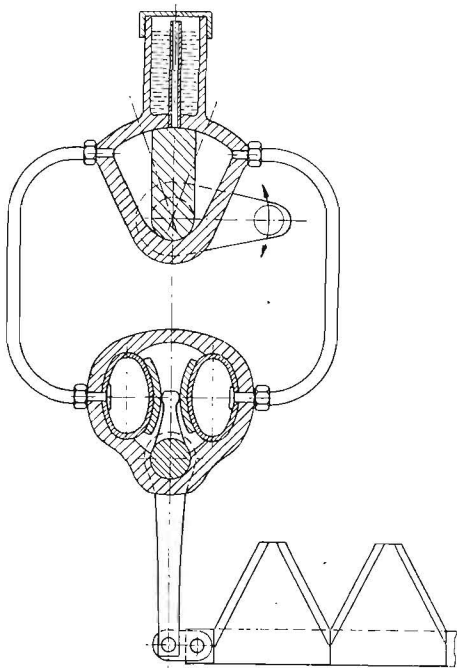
Schwingtrieb mit Flügelpumpe und Membranmotor
